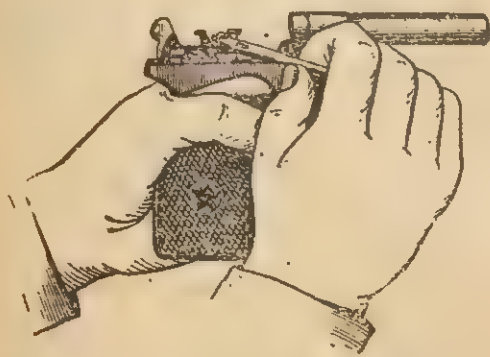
Снятие крючка пружины шептала с затворной задержки
